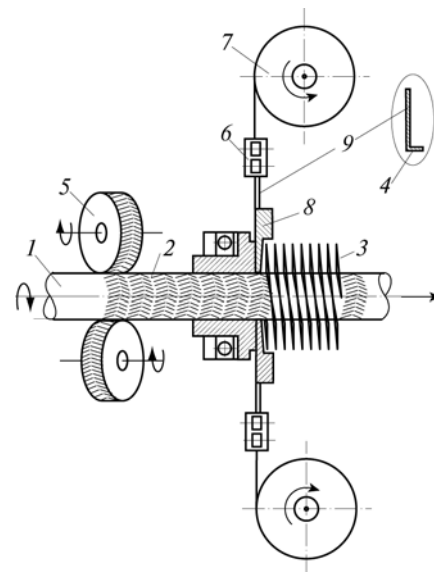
Процесс изготовления БРТ с шевронным рифлением и двухзаходными ребрами
